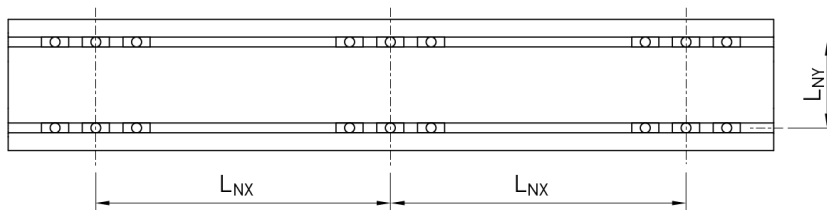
Befestigung mit Nutensteinen – HT250S
